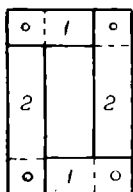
Asamblarea miezului în sâmbure din benzi prin suprapunere.
